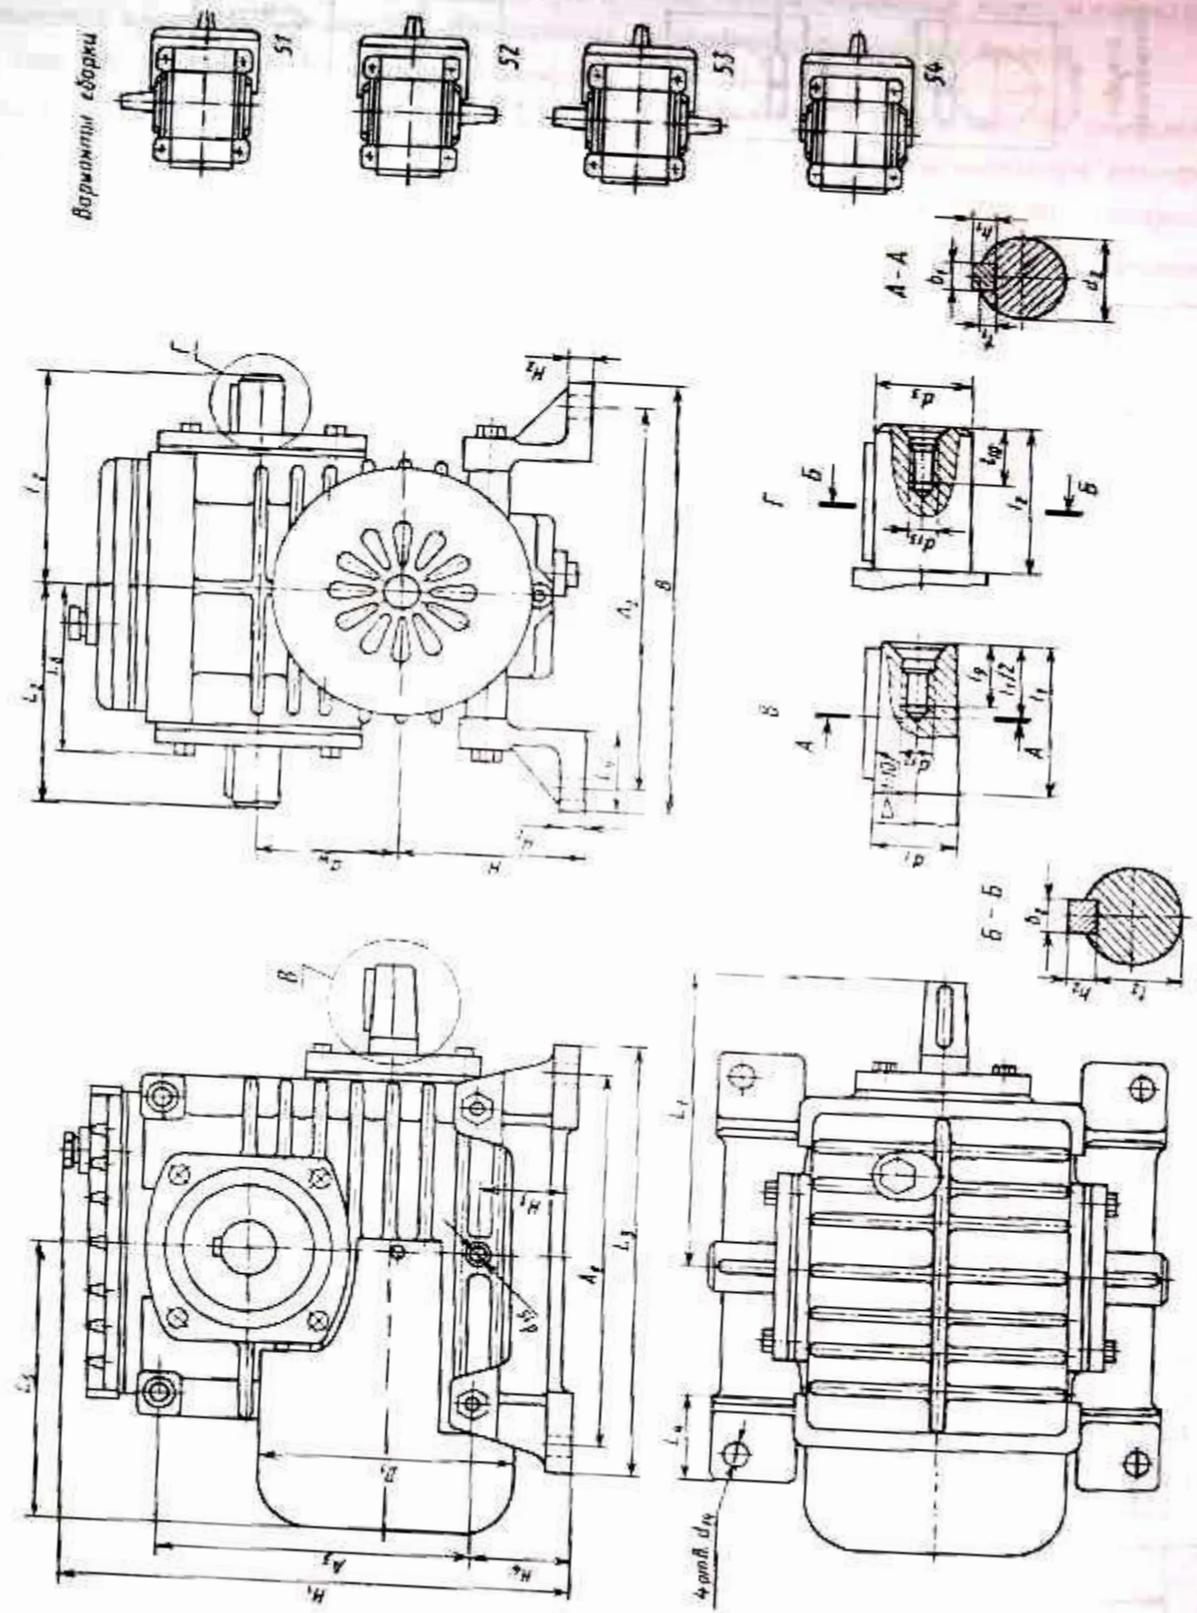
Редукторы Ч-50, Ч-63, Ч-80
